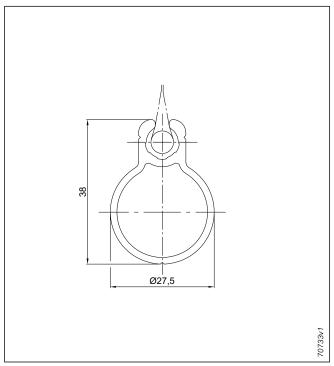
Fallprofil Ø27,5 mm mit Nut (Standard)
